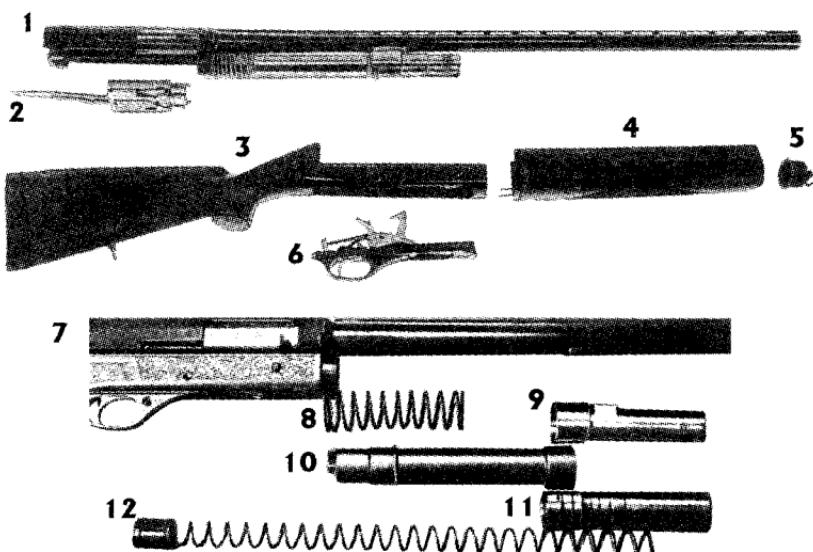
Узлы и детали ТОЗ-87 при неполной разборке: 1 – ствол с крышкой, газовым узлом и магазином; 2 – затворная рама; 3 – приклад с коробкой; 4 – цевье; 5 – колпачок цевья; 6 – ударно-спусковой механизм; 7 – ружье в сборе; 8 – пружина; 9 – камера газовая; 10 – трубка магазинная; 11 – поршень; 12 – пружина магазина с одним толкателем.
